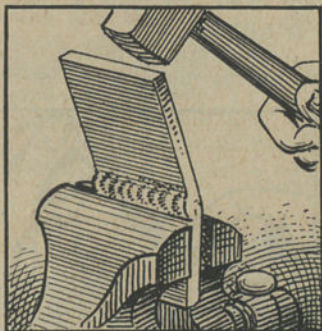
Dobradura duma soldadura revelando a falta de penetração, causa de ruptura e colagem.
